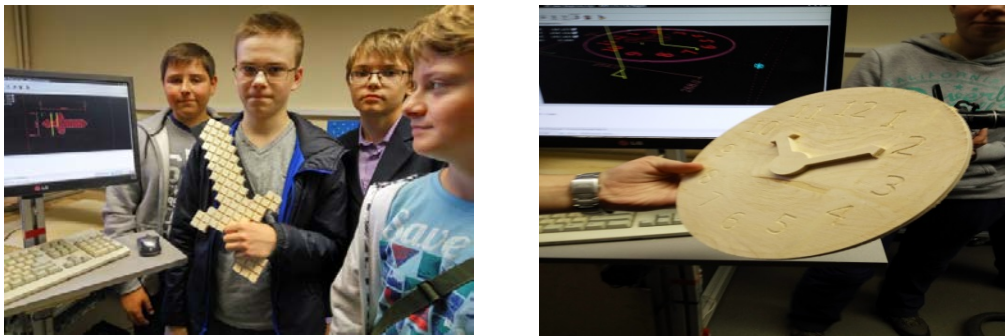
3D-моделирование деталей и их изготовление на станках с ЧПУ на кафедре «Металлорежущие станки»
